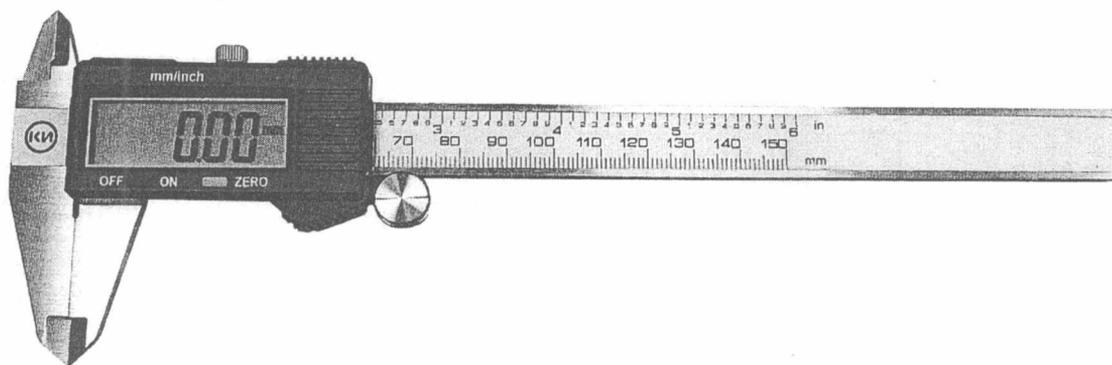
Общий вид штангенциркулей типа ШЦЦ-I
